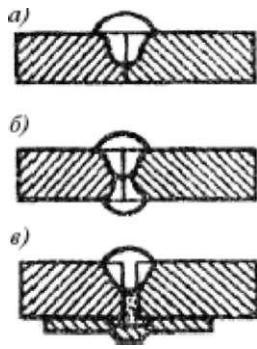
Выполнение стыкового шва двухсторонней автоматической сваркой: а - сварка первого шва на весу; б - сварка второго шва с перекрытием первого шва на 3—4 мм; в - сварка первого шва на флюсо-медной подкладке
